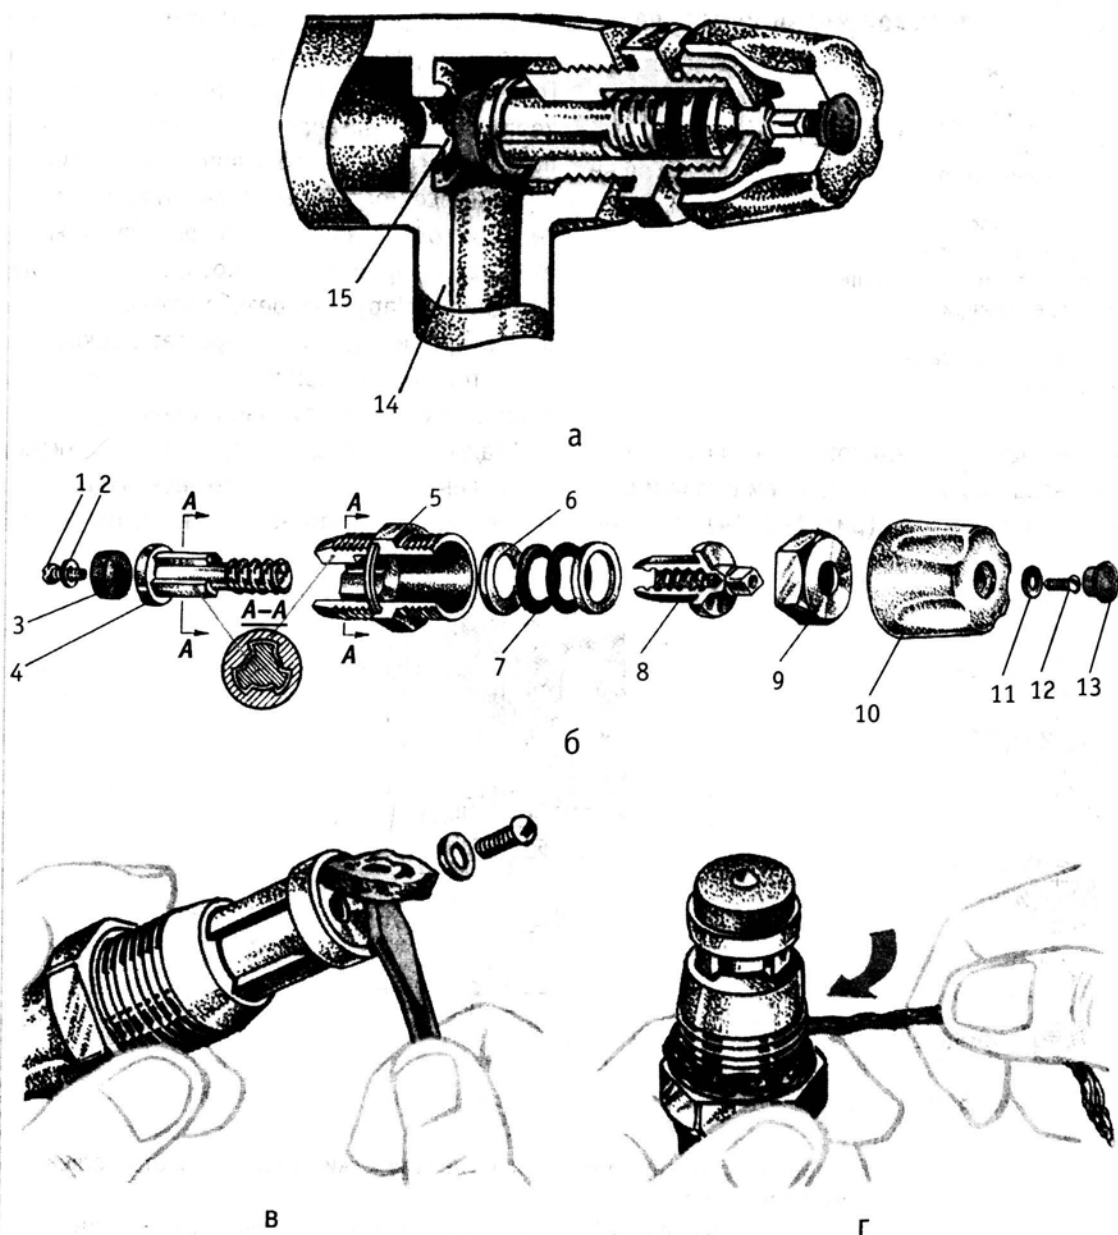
Вентильная головка с возвратно-поступательным движением трехпазового шпинделя:
